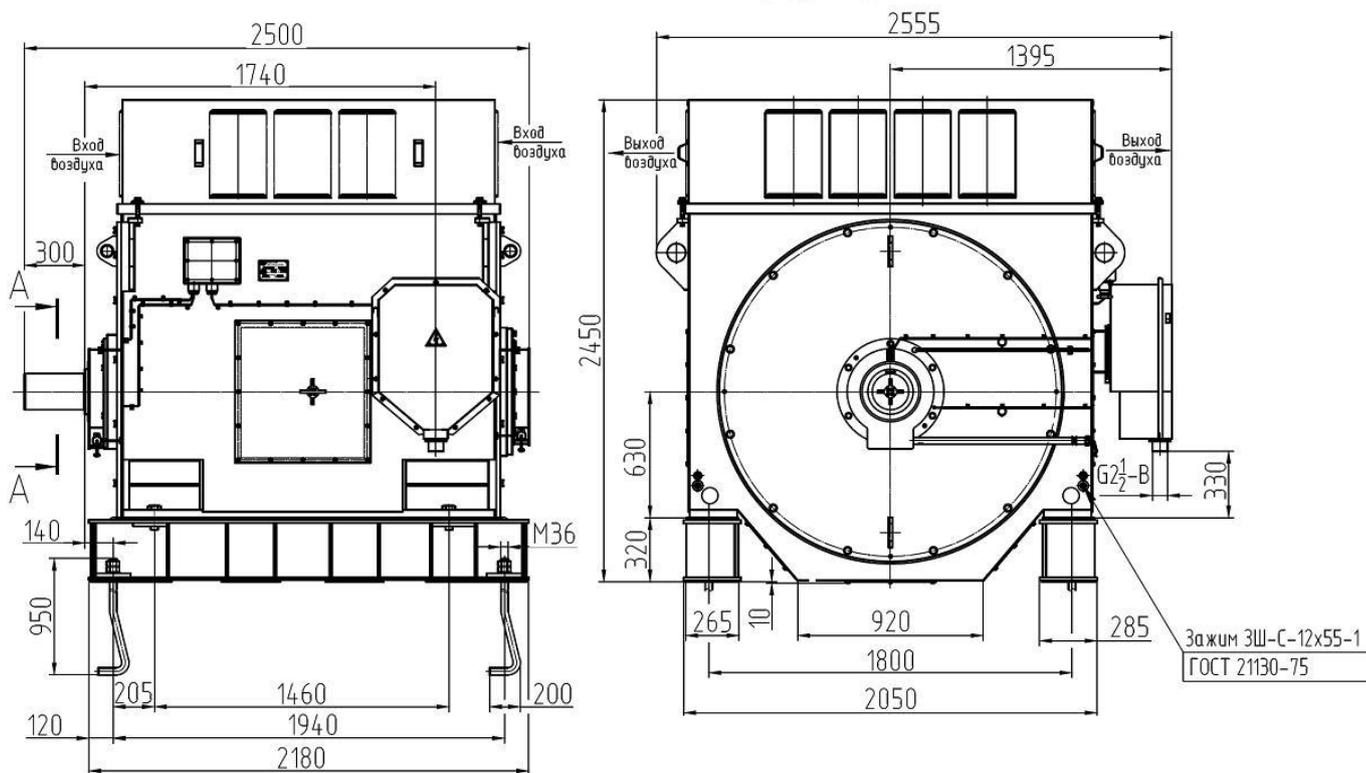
Габаритные и присоединительные размеры двигателей АД-500-16ТС3.
